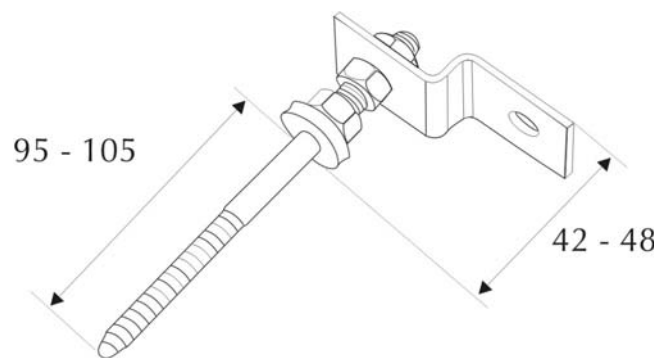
Fixation pour toiture inclinée, tôle ondulée
